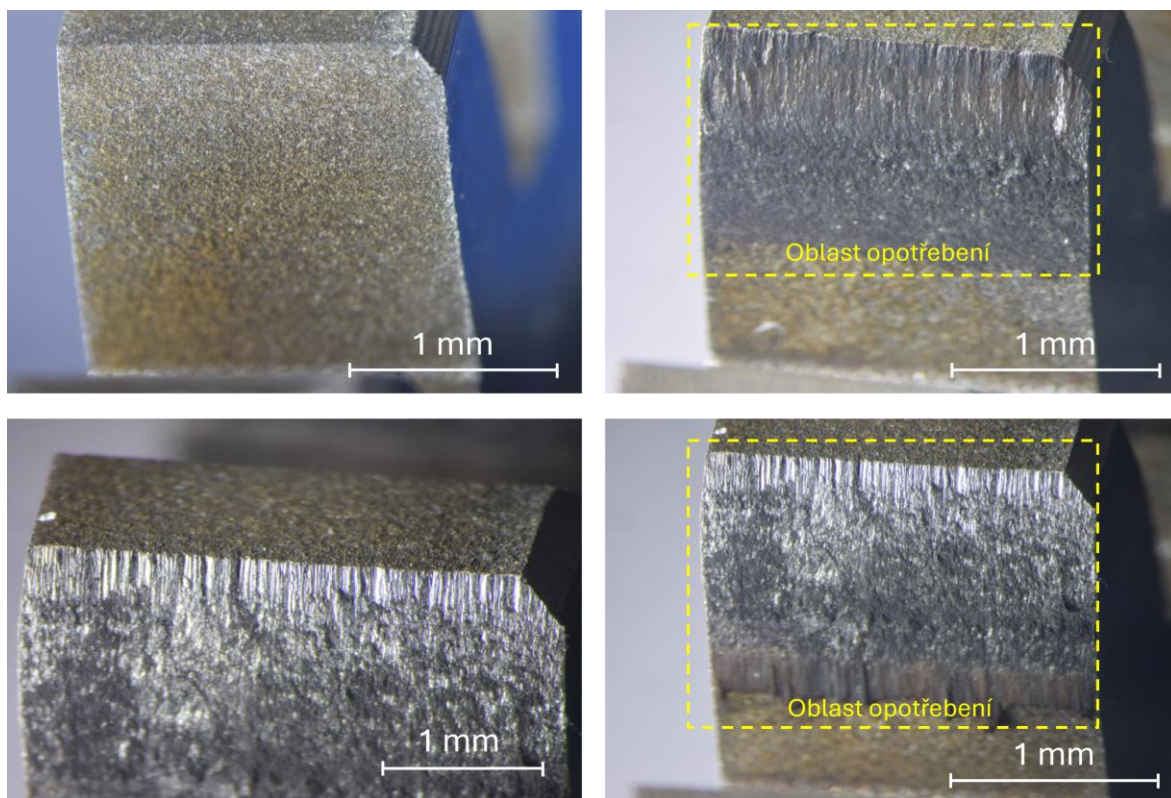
Detail povrchu testovaného pastorku před (vlevo) a po testu (vpravo) – test V2
